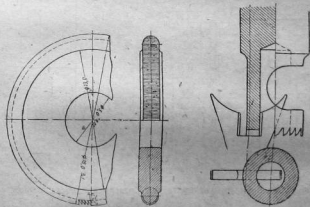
Полуавтомат Джиак и Хазлер для фрезеровки пазов анкера.
